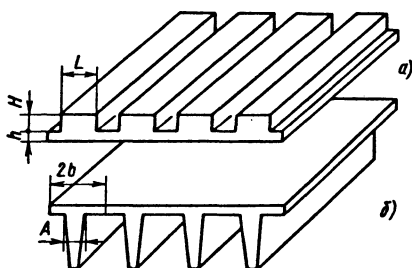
Заготовка после первого перехода (а) и готовая поковка с ребром (б)
